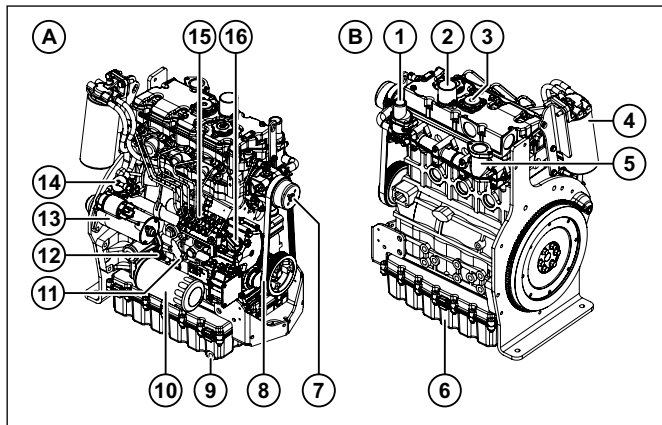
Dieselmotorbaugruppen (Perkins-Dieselmotor)
